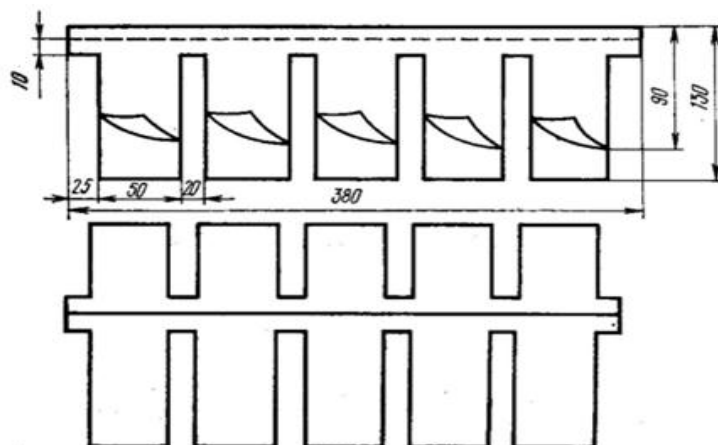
Схема изготовления проб для испытаний при приложении растягивающей нагрузки поперёк строчки
